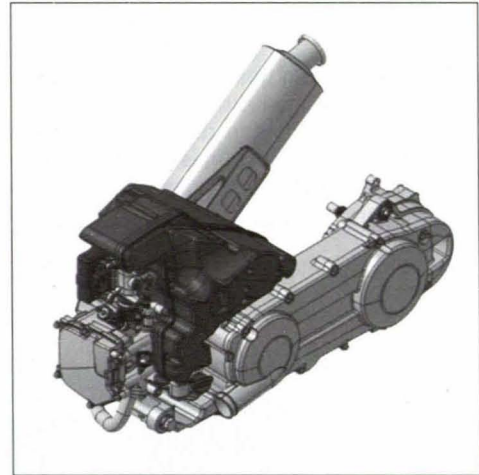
Kurbelgehäuseaufgeladener 4-Takt Motor
